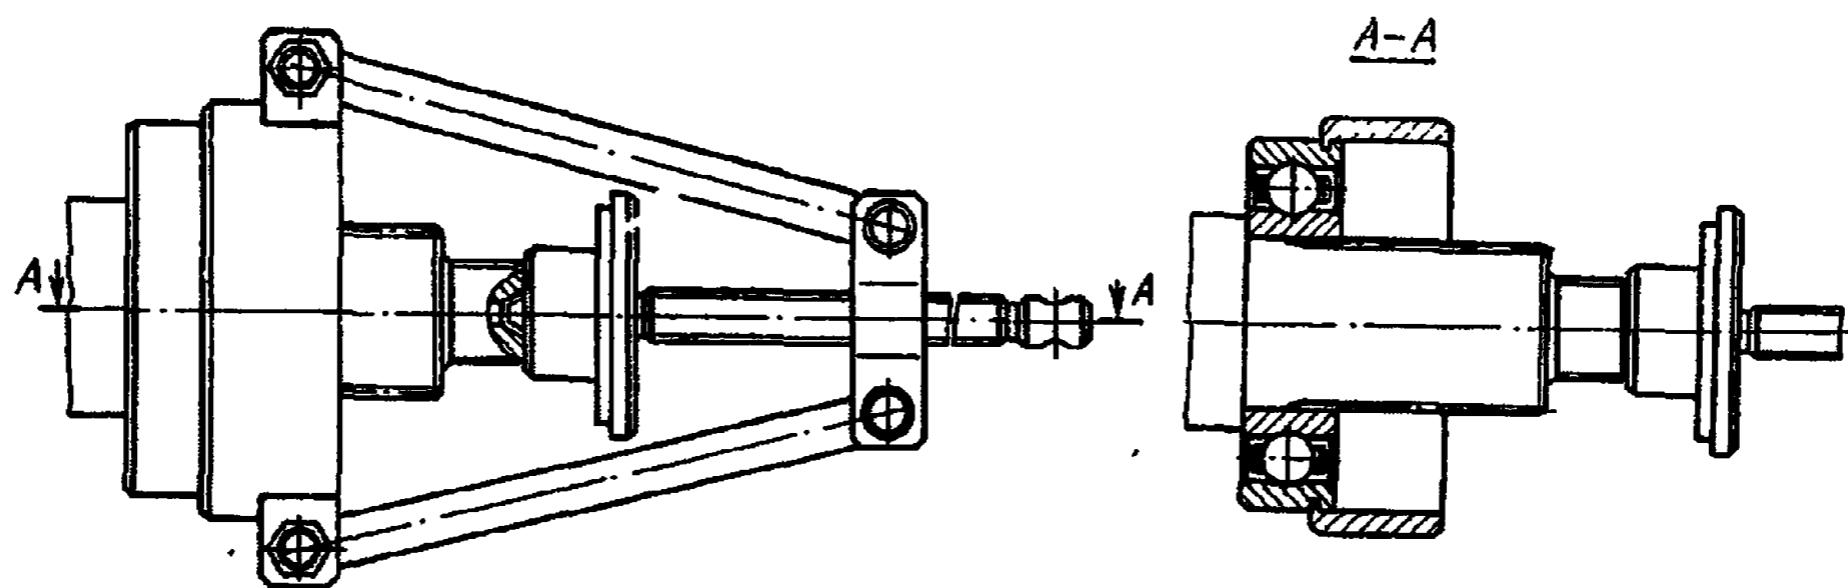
Снятие подшипника зубчатого колеса привода заднего моста
